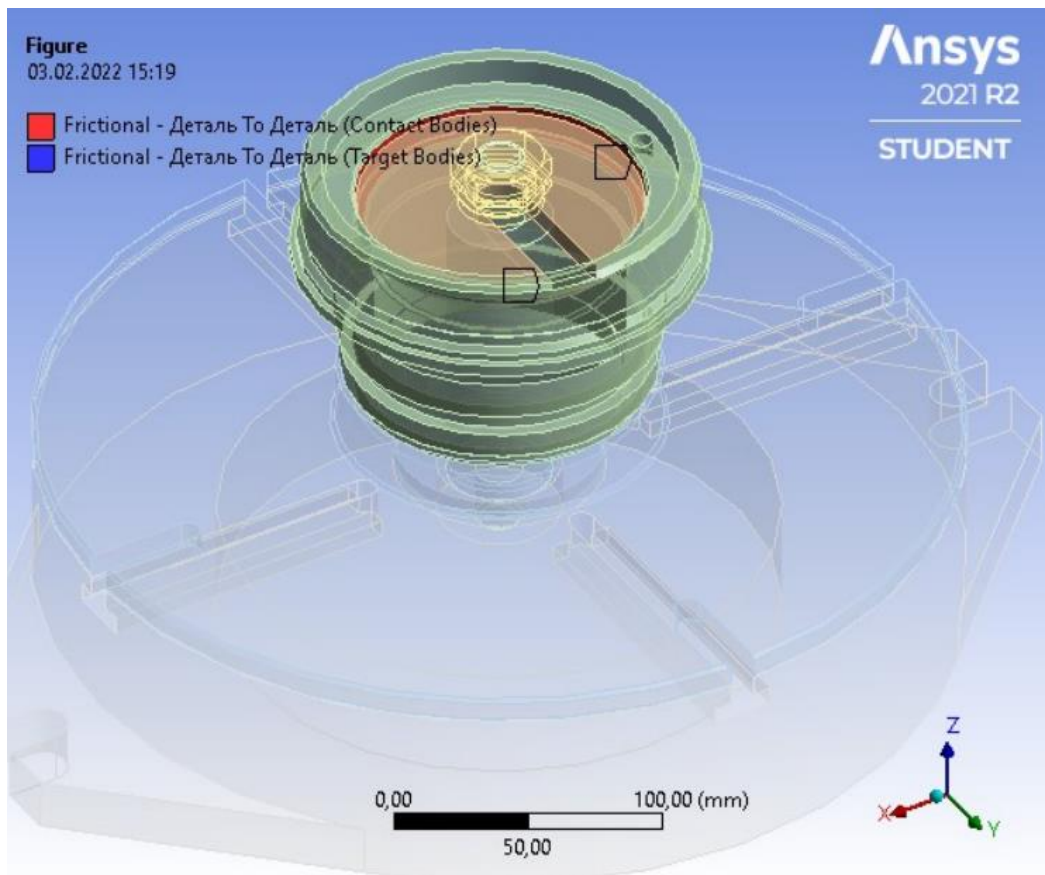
Сполучення поверхонь в системі «заготовка-прихват»
